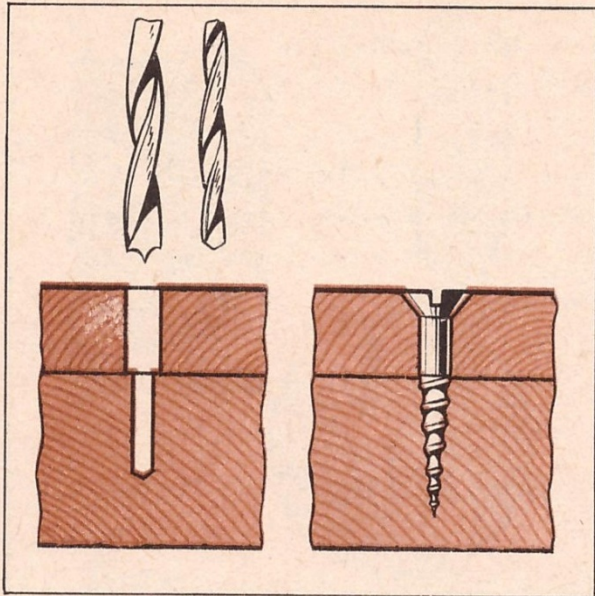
Сверление отверстия под шуруп двумя сверлами.
